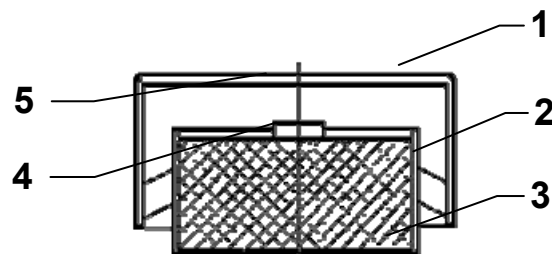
Конструкція генератора ОСА-М з коаксиально розташованими напівкорпусами:
